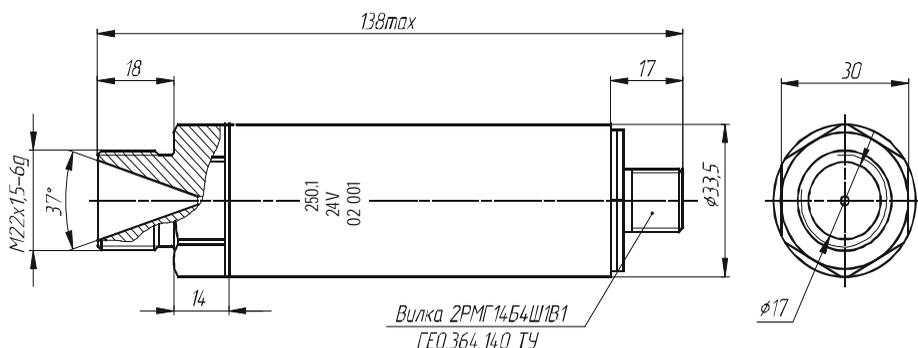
Габаритные и присоединительные размеры датчика давления
